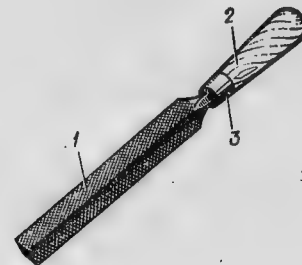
1 — напильник; 2 — ручка; 3 — колпачок
